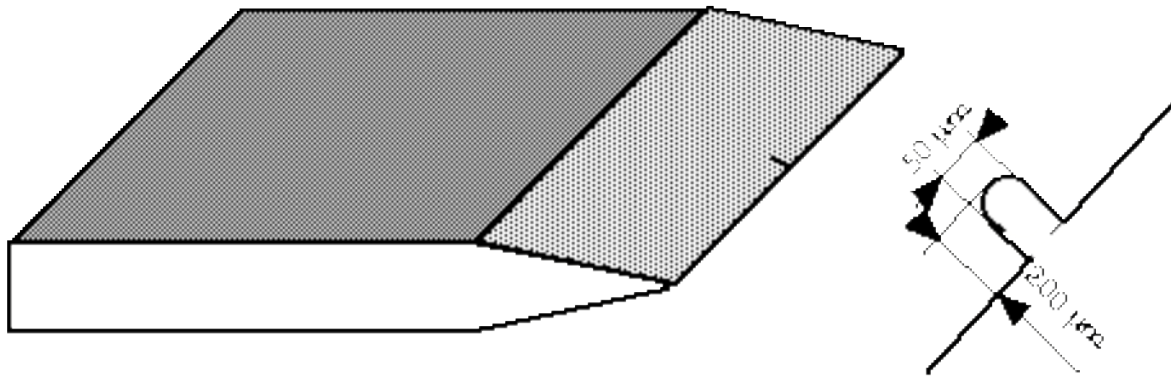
Géométrie et dimensions de l'entaille réalisée sur éprouvette de fatigue thermique
